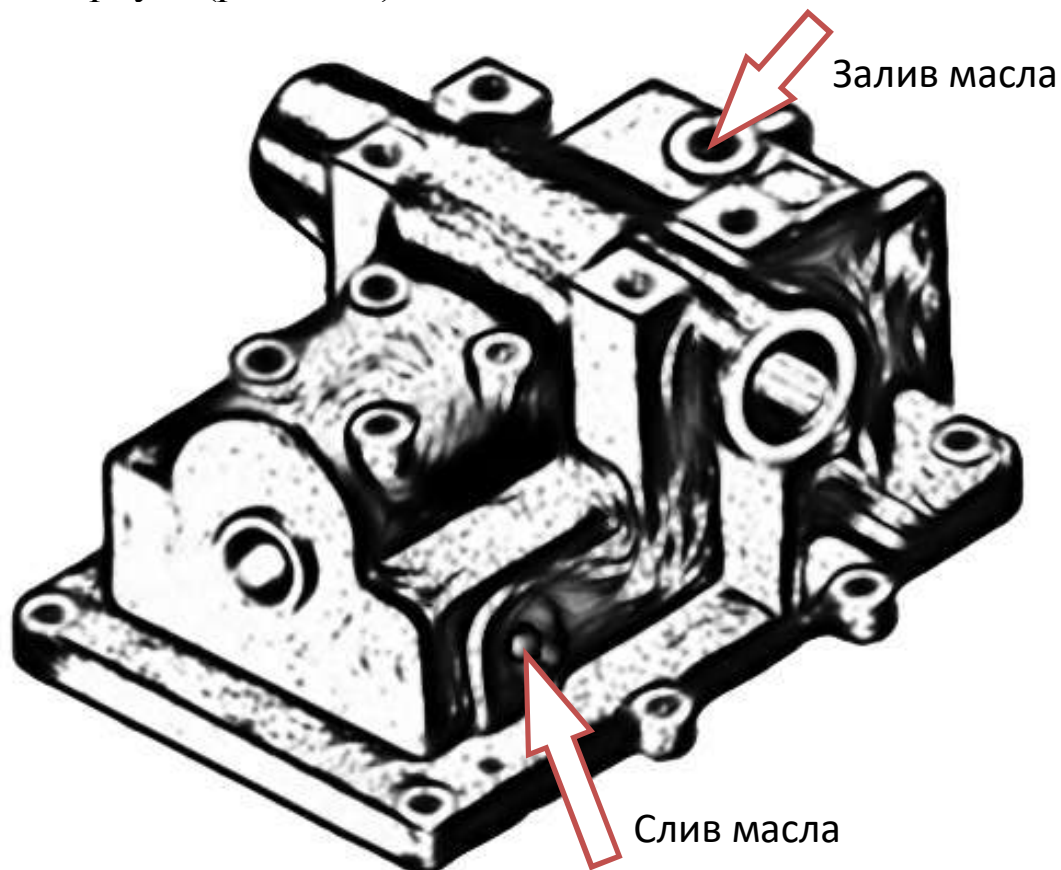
Заливное и сливное отверстия на корпусе гидробака.
